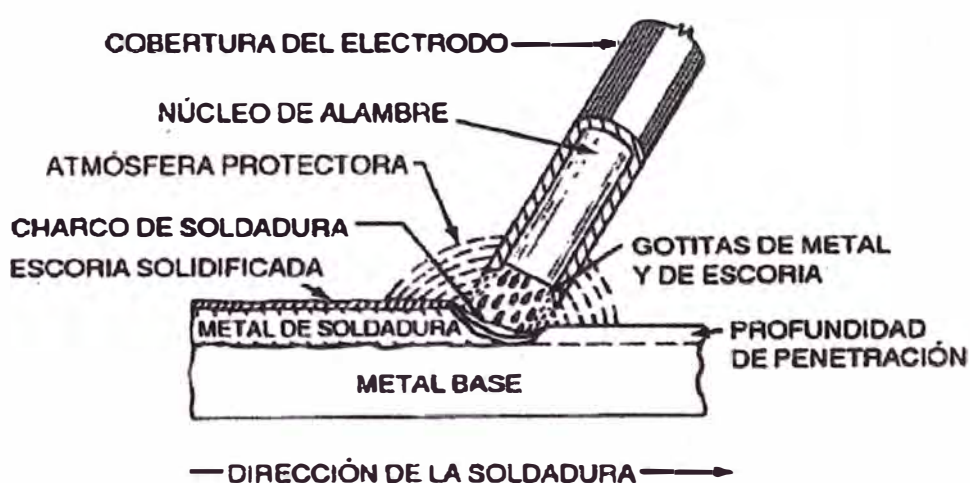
Acción protectora del arco en la soldadura por arco de metal protegido
